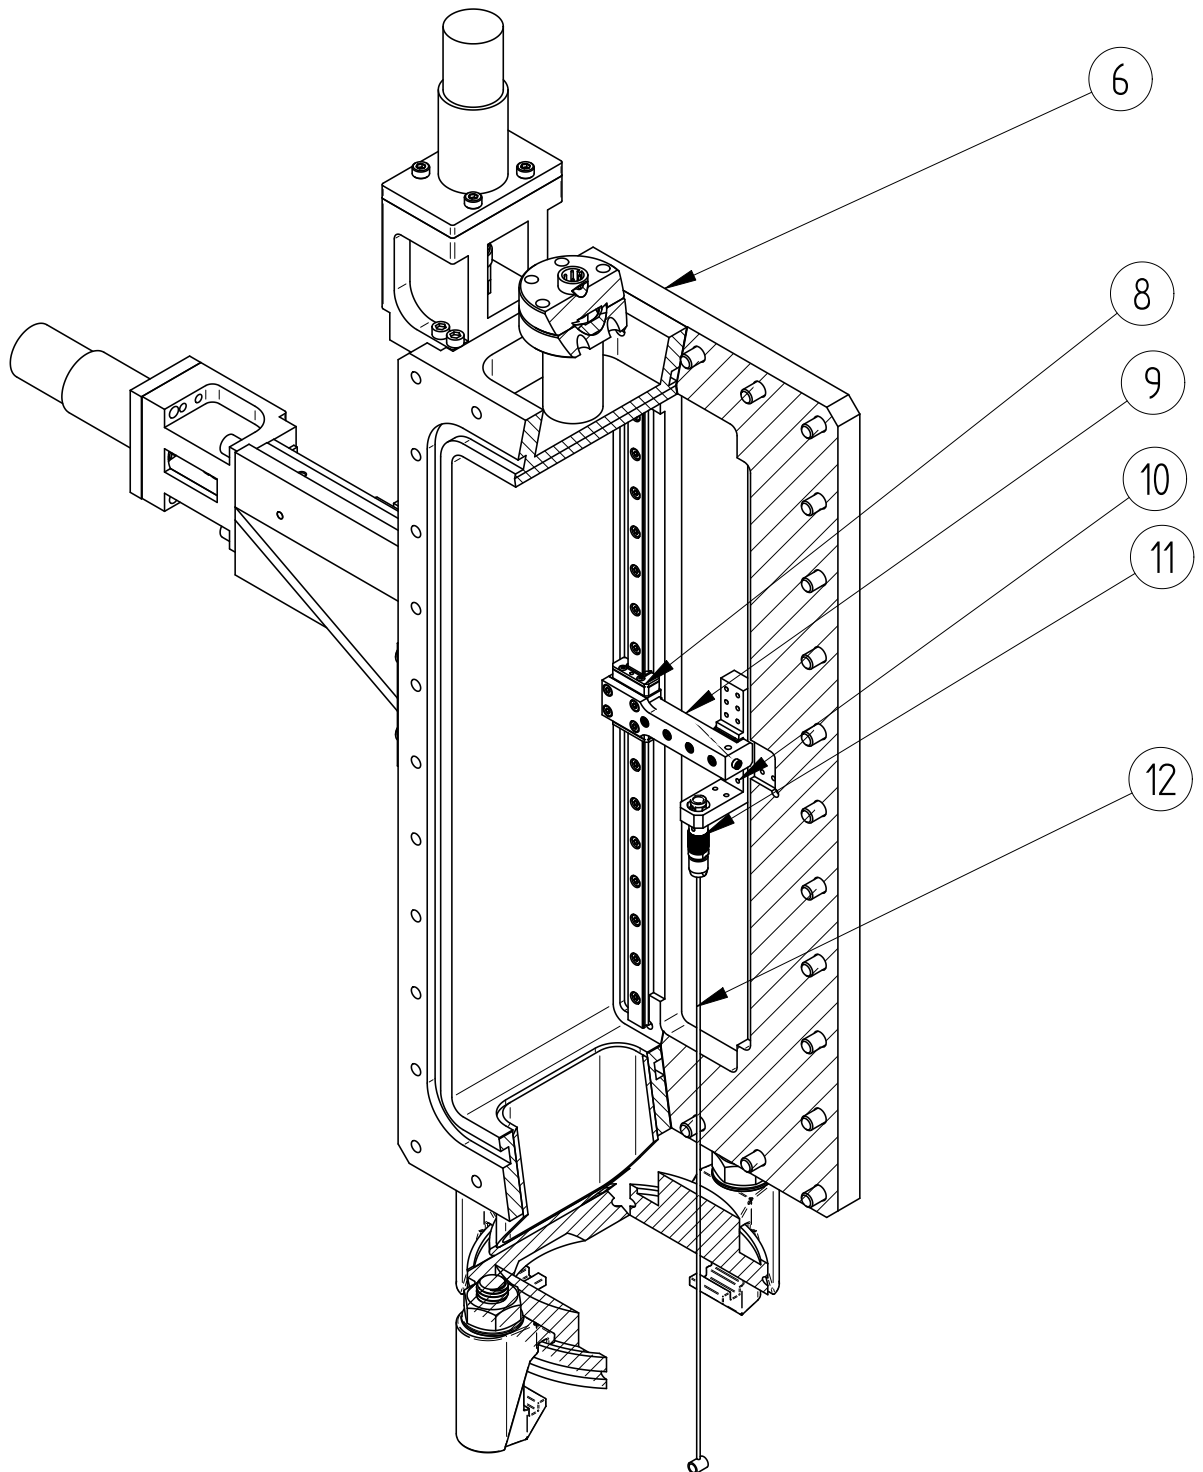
isometrische Ansicht des Beamstop Device mit geschnittener Vakuumkammer
